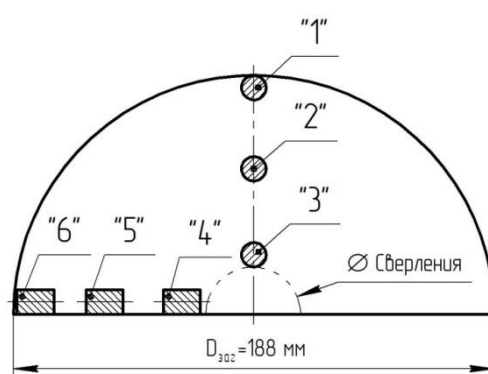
Схема отбора образцов из темплета заготовки из стали 10X13H3MФБ (сверление Ø 40 мм)
